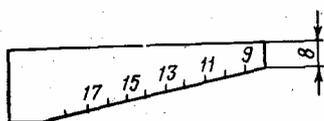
Шаблон для замера разрыва контактов переключателей ТК-36Т, РК-022Т, МКП-23 и провала контактов ТК-36Т, РК-022Т
